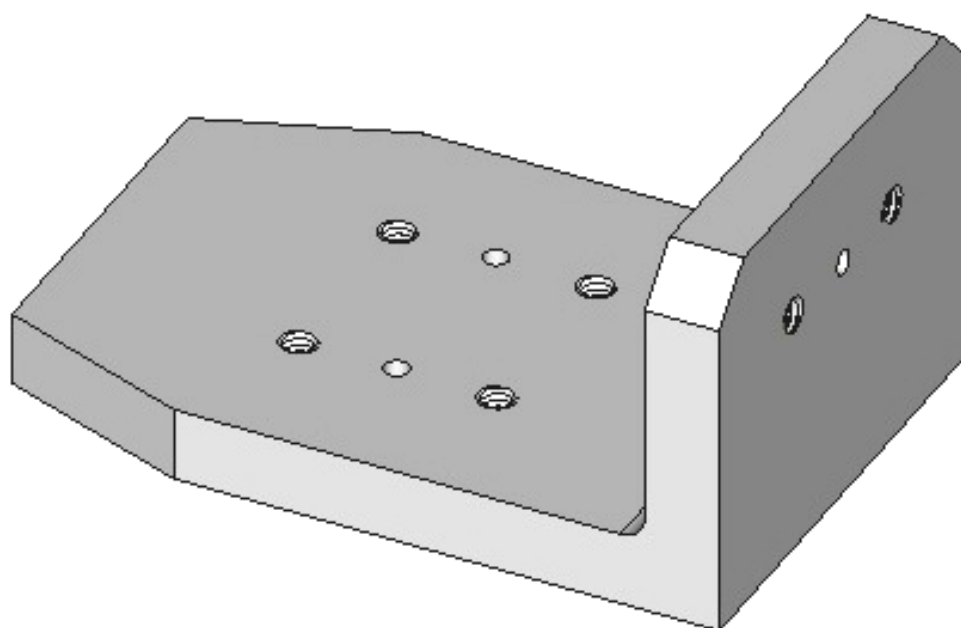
Вариант «Уголок» исполнения монолитного корпуса
